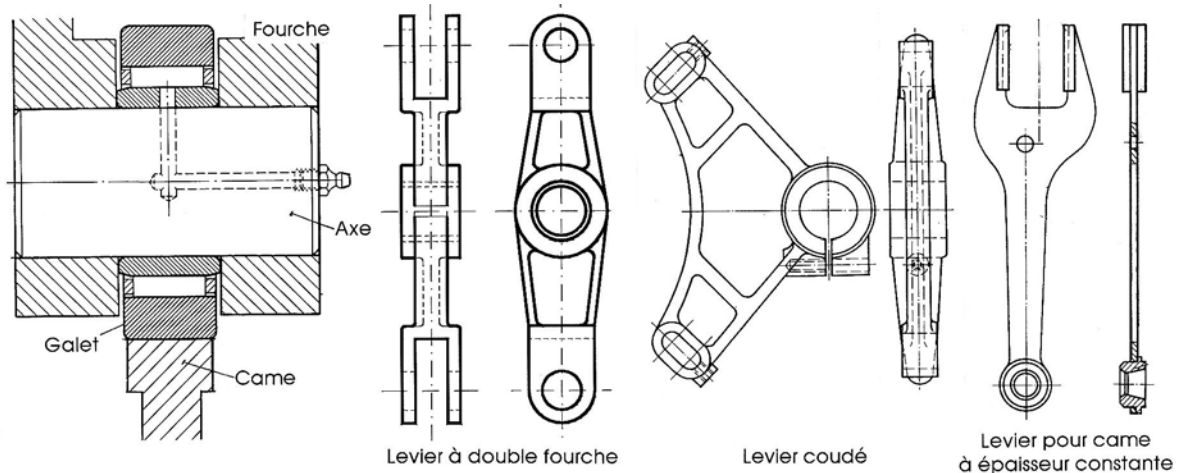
Exemples de montage d'un galet et leviers pour mécanismes à cames
